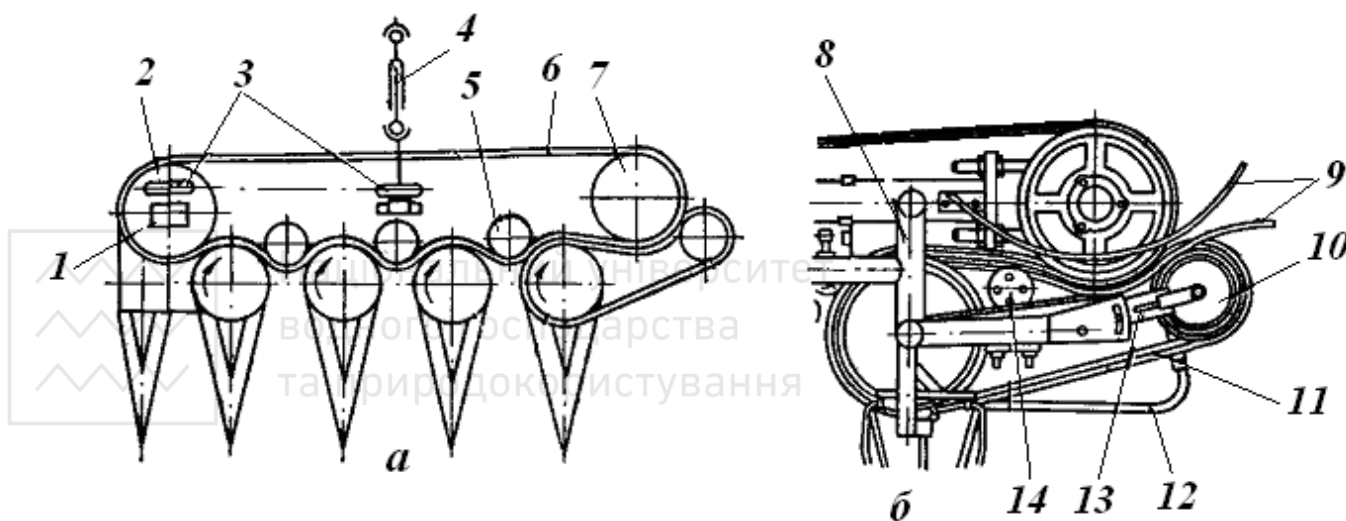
Льонобралка фронтальна начіпна ТЛН-1,5А: *а* - функціональна схема; *б* - вивідний пристрій; 1 - редуктор; 2 - шків ведучий; 3 - передача ланцюгова; 4 - передача карданна; 5 - ролик притискний; 6 - пас бральний основний; 7 - шків натяжний; 8 - рама; 9 - прутки; 10 - піків вивідний; 11 - пас вивідний; 12 - пруток; 13 - натяжний пристрій; 14 - ролик притискний; 15 - подільник; 16 - шків бральні
